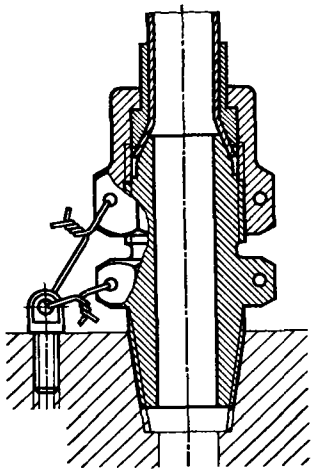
Стопорение вязкой шпильного соединения (шпильер и накладную гайку стопорят вязкой к корпусу)
